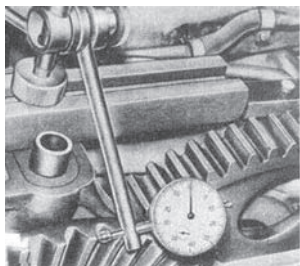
Проверка бокового зазора в зубьях шестерен главной передачи.
